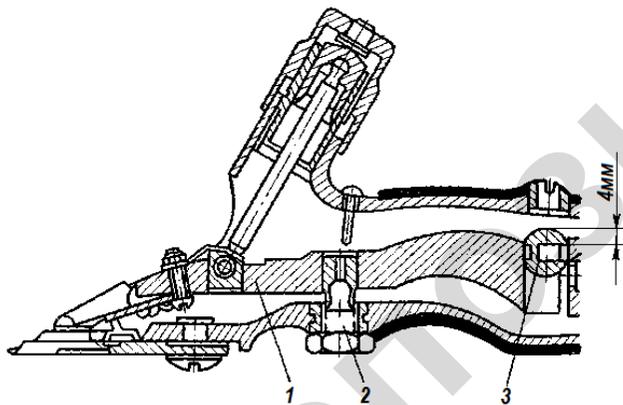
Регулировка положения рычага в корпусе машинки:
